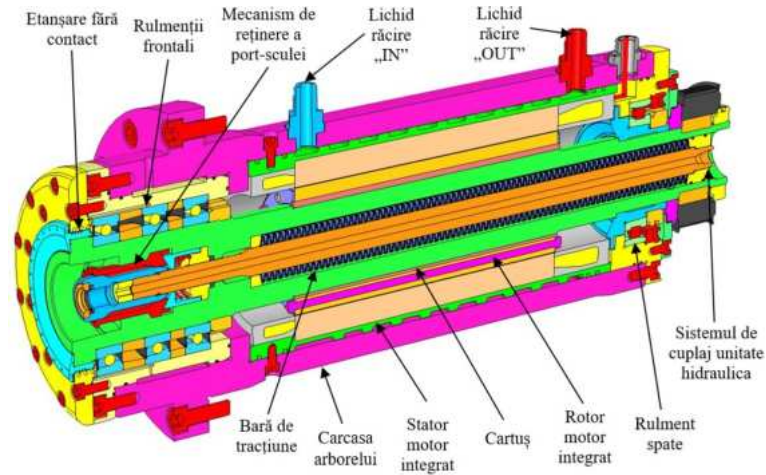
Componentele principale dintr-un AP cu motor integrat
